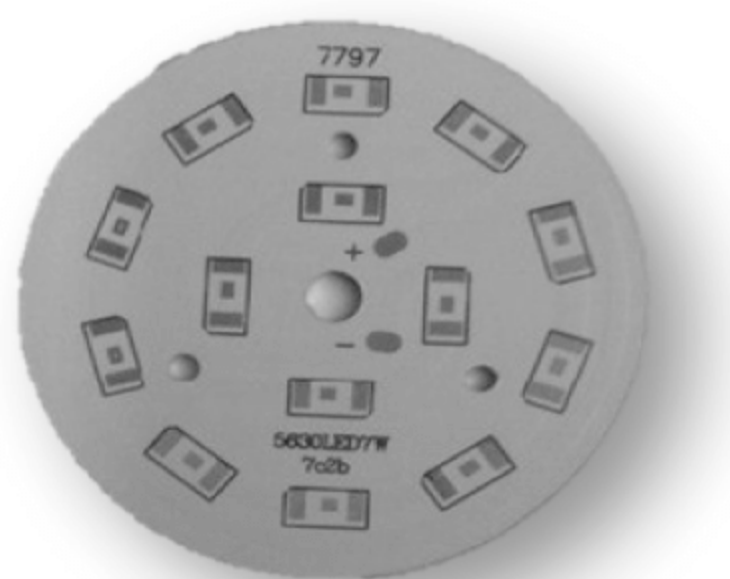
一种球泡灯 PCB 灯板(铝基板)
